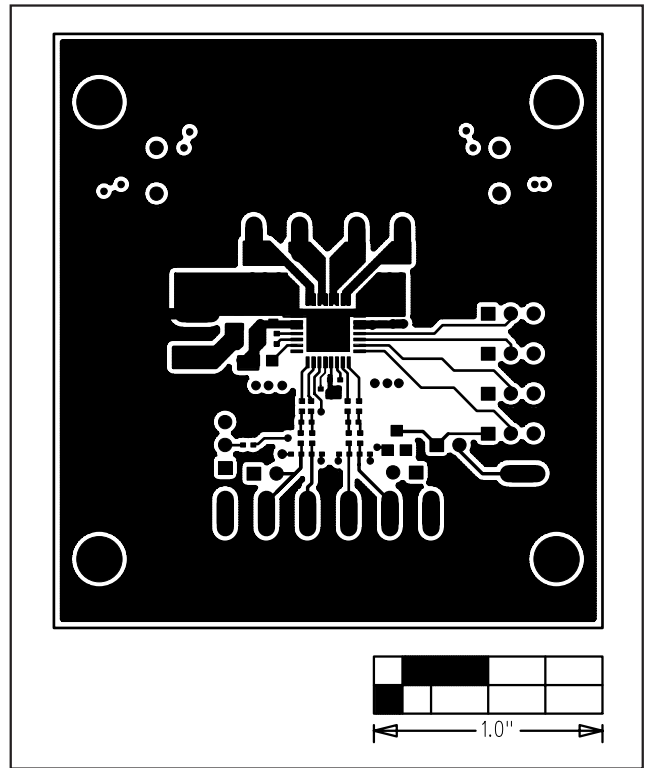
MAX9714 EV 키트 PCB 레이아웃 — 부품 측
